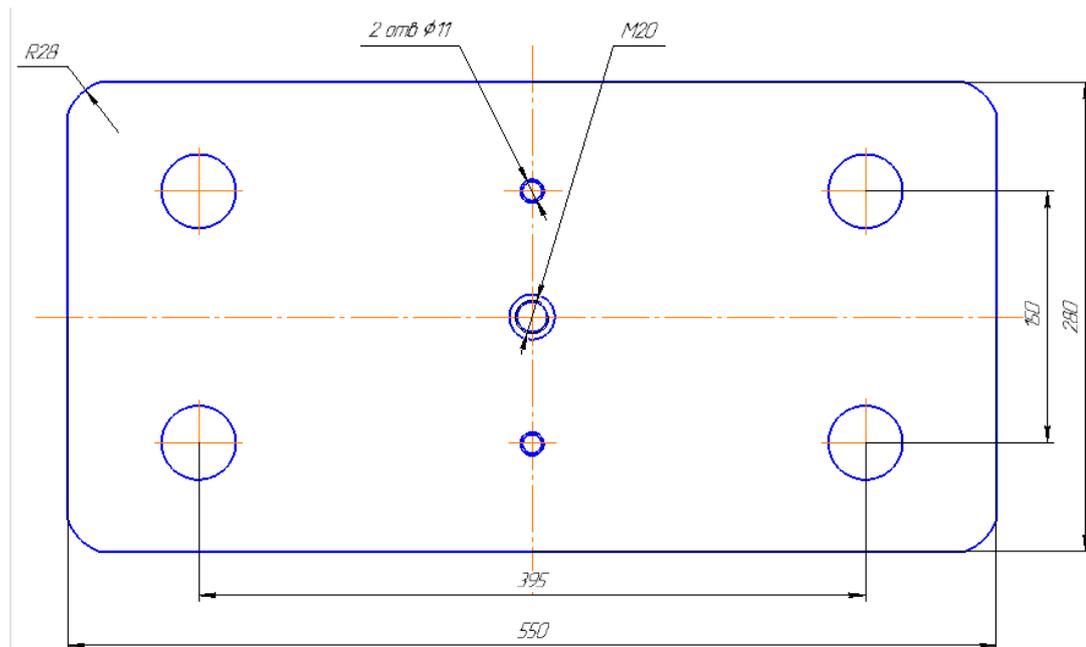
Эскиз детали «Крышка шатуна прессы»
